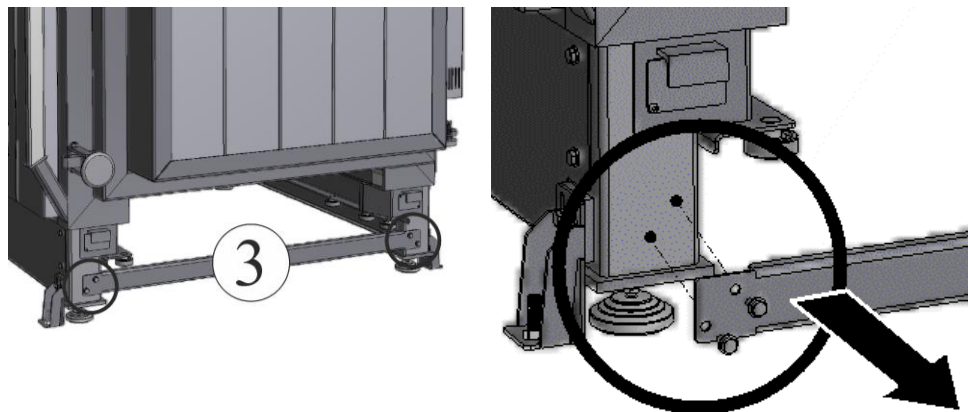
Удаление транспортировочной штанги (рисунок примерный)
